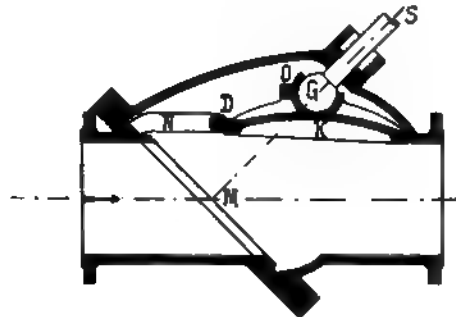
Eckstück mit Klappe und Schraubenspindelsperung
